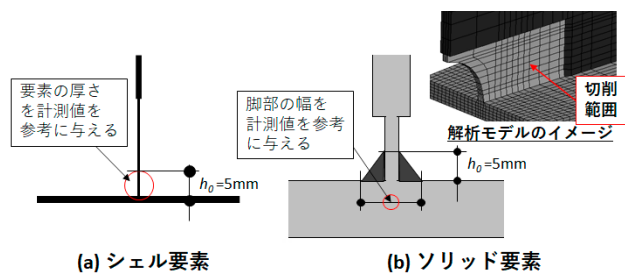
余盛のモデル化 (View of Excess Weld Metal)
